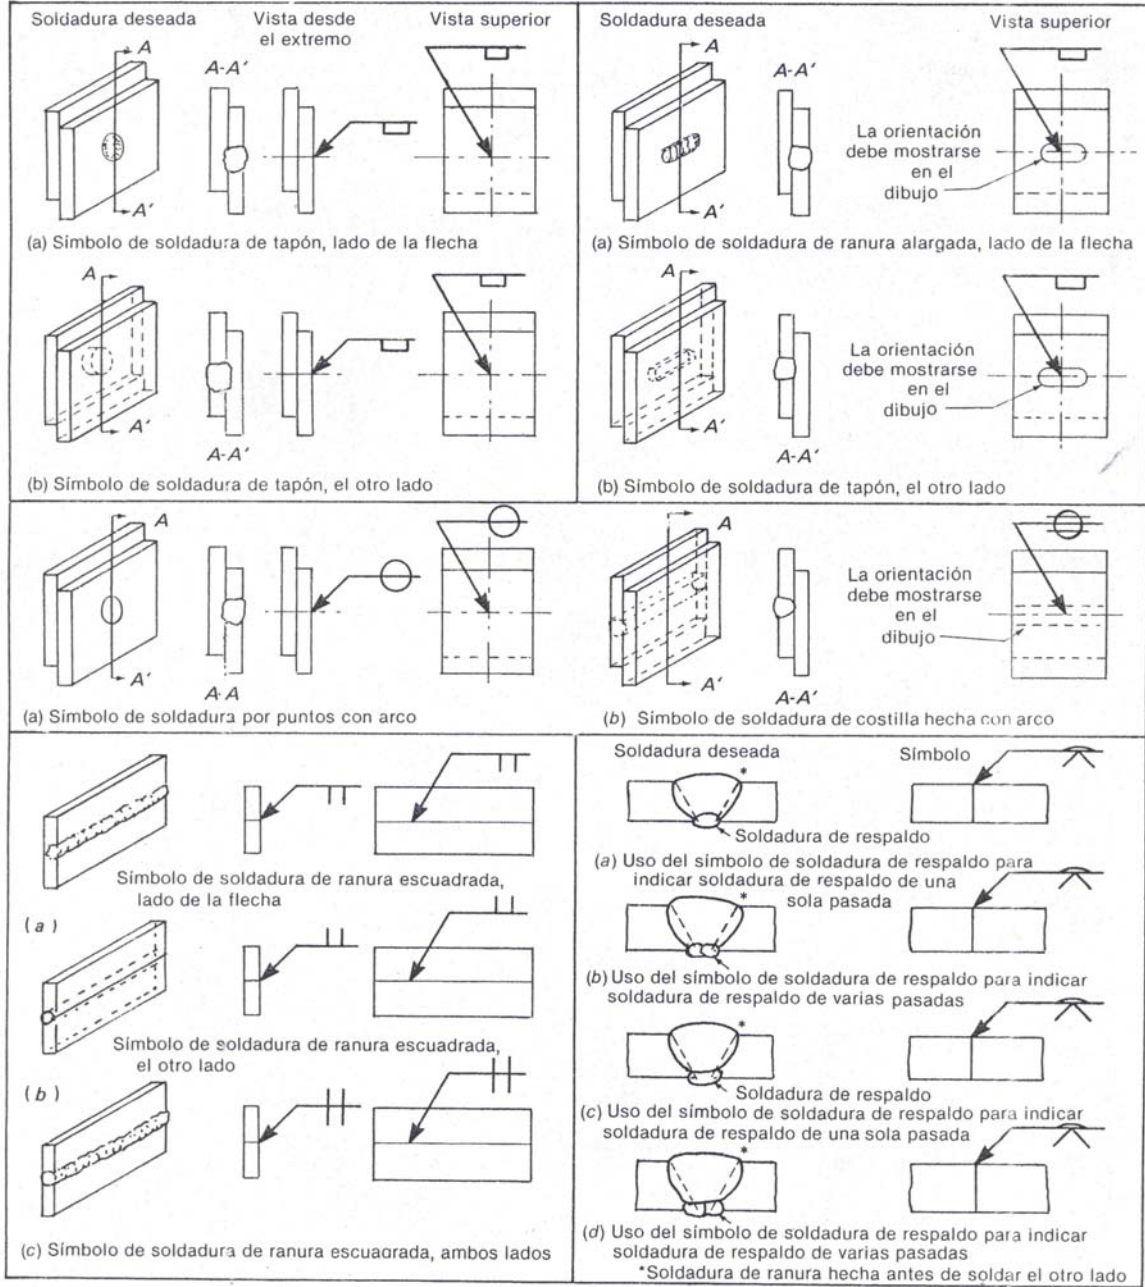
Ejemplos de símbolos de soldadura y las soldaduras que representan.
